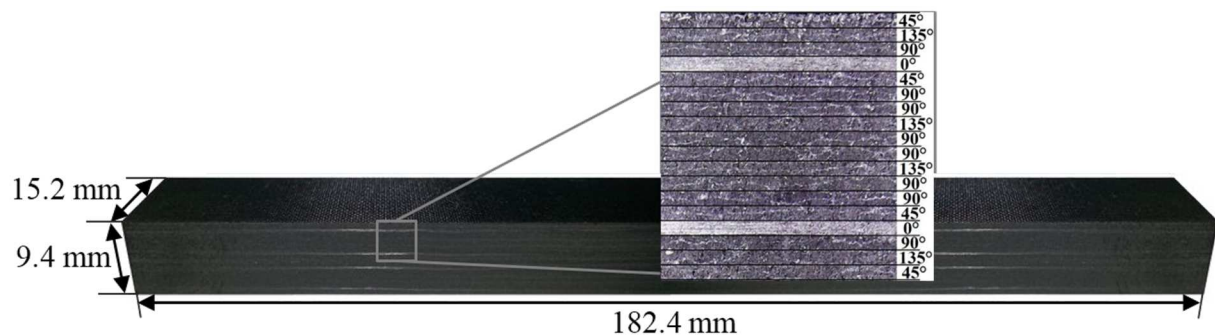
Dimensions et séquence d'empilement des éprouvettes.
